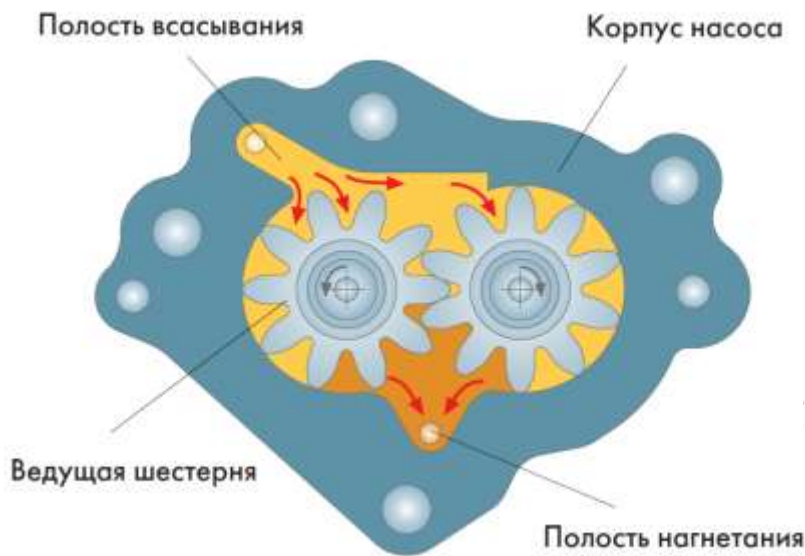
Устройство шестеренного топливоподкачивающего насоса ТНВД BOSCH CP1H [6].
